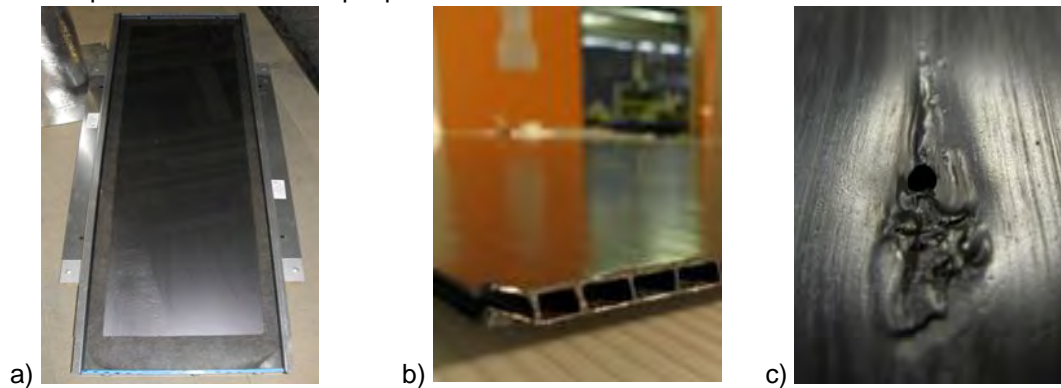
a) vue générale d'une plaque extrudée en PPS, b) vue des canaux en coupe, c) vue d'un défaut avec trou débouchant.
